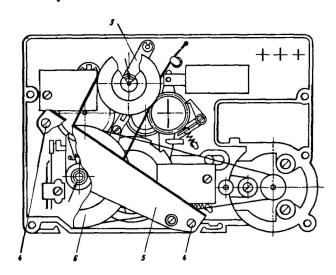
Внешний вид ЛПМ (вид сверху). Места смазки ЛПМ (→)
